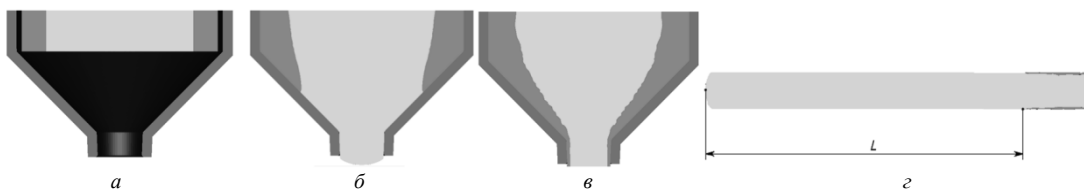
Стадии процесса прессования биметаллической заготовки и вид переднего монометаллического конца (L – длина переднего монометаллического конца): a – начало прессования; b – окончание распрессовки заготовки; c – установившийся процесс прессования биметаллической заготовки; d – вид переднего конца
